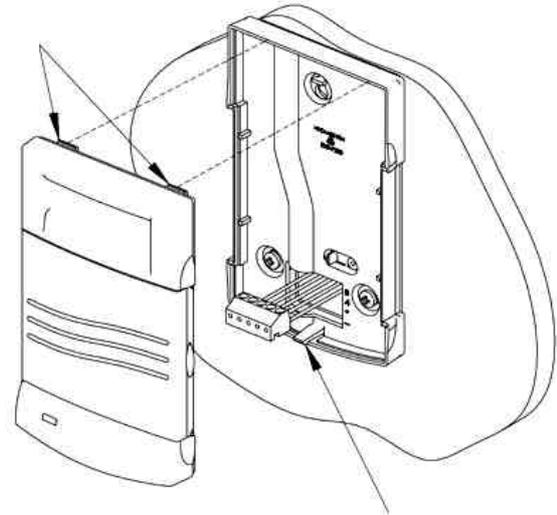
Aufsetzen und Einrasten der oberen Gehäusebaugruppe
